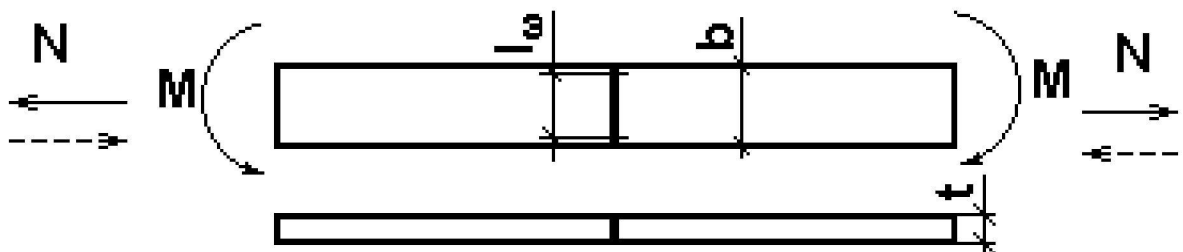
К расчету стыкового сварного шва
